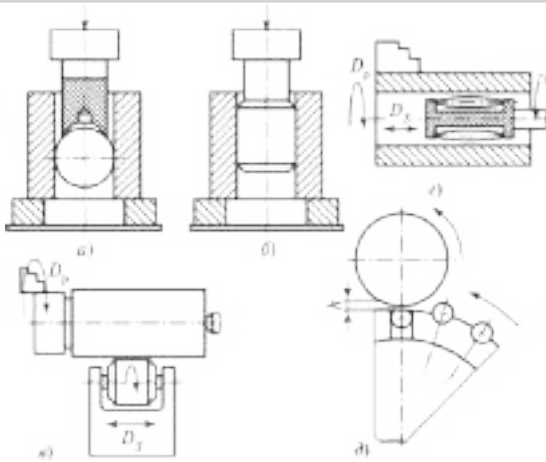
Методи обробки пластичним деформуванням: а — калібрування отвору; б — дорнування (інструмент — дорн); в — обкатування; г — розкатування; д — наклепування поверхні кулькою
